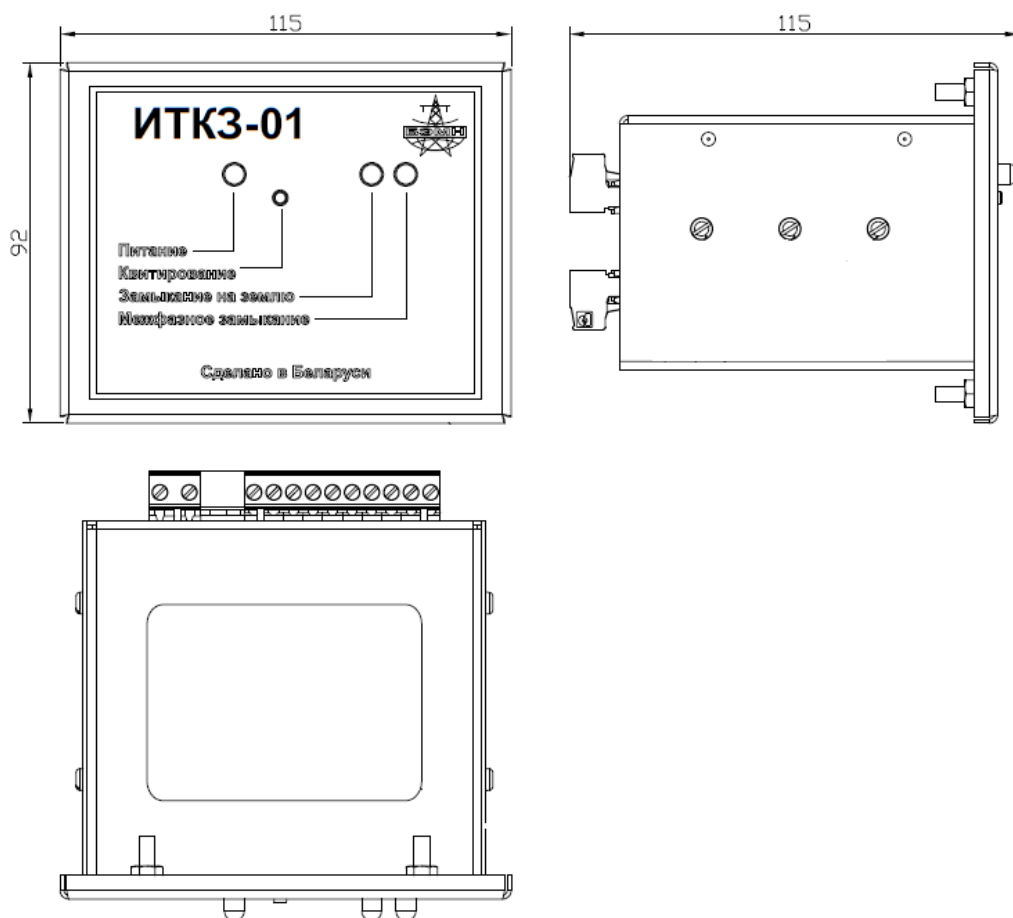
Габаритные размеры ИТКЗ-01
